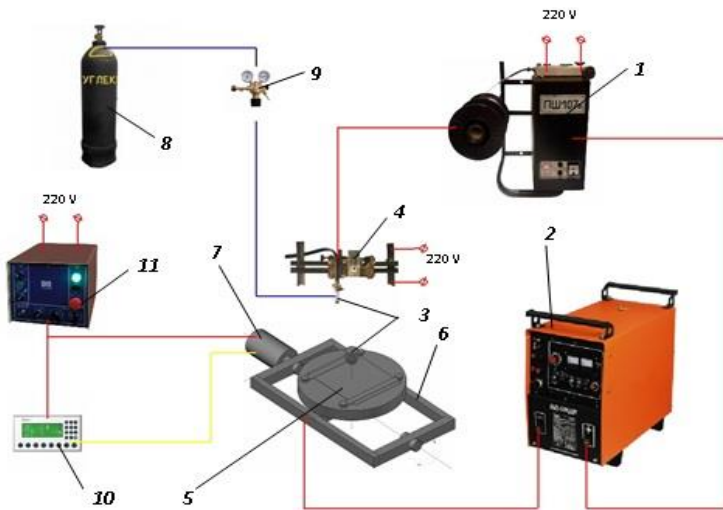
Структурна схема установки для наплавлення: 1 – півавтомат зварювальний; 2 – джерело живлення; 3 – зварювальний пальник; 4 – рухома станина; 5 – деталь що наплавляється; 6 – коливальний стіл; 7 – кроковий двигун; 8 – балон газовий; 9 – редуктор газовий; 10 – пульт керування; 11 – блок керування. Червона – силова магістраль; Блакитна – газова магістраль; Жовта – магістраль програмування
